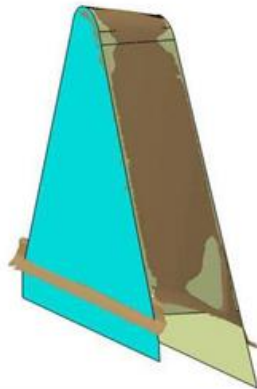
Illustration des plans de base de la dent de la fraise-mère (face de coupe et l'arrière de la dent).
